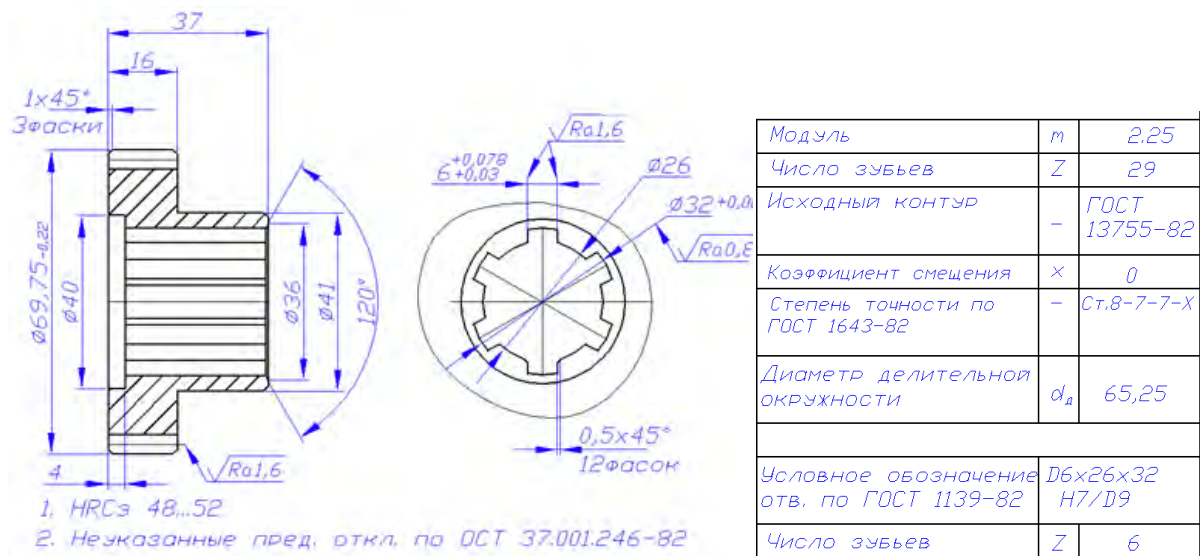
Чертеж шестерни из стали 16ХЗНВФБМ-Ш
